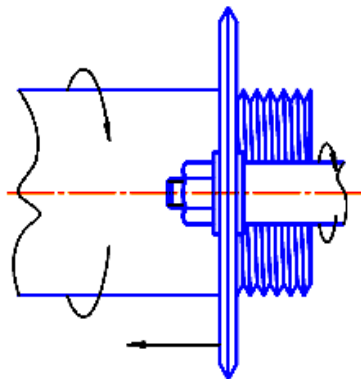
Схема шлифования наружной резьбы однопрофильным шлифовальным кругом
